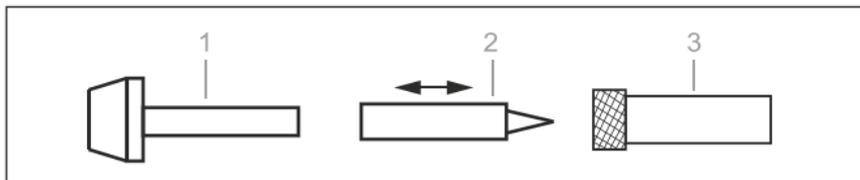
Insertar o cambiar las puntas de soldadura
